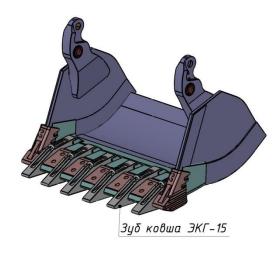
Монтаж режущей кромки под зуб ковша ЭКГ-15 с бокорезами и накладками
